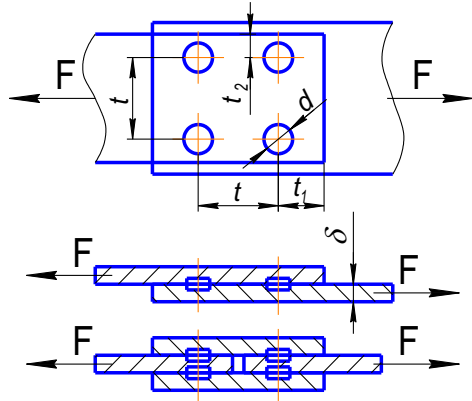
Розрахункова схема точкового зварного з'єднання
